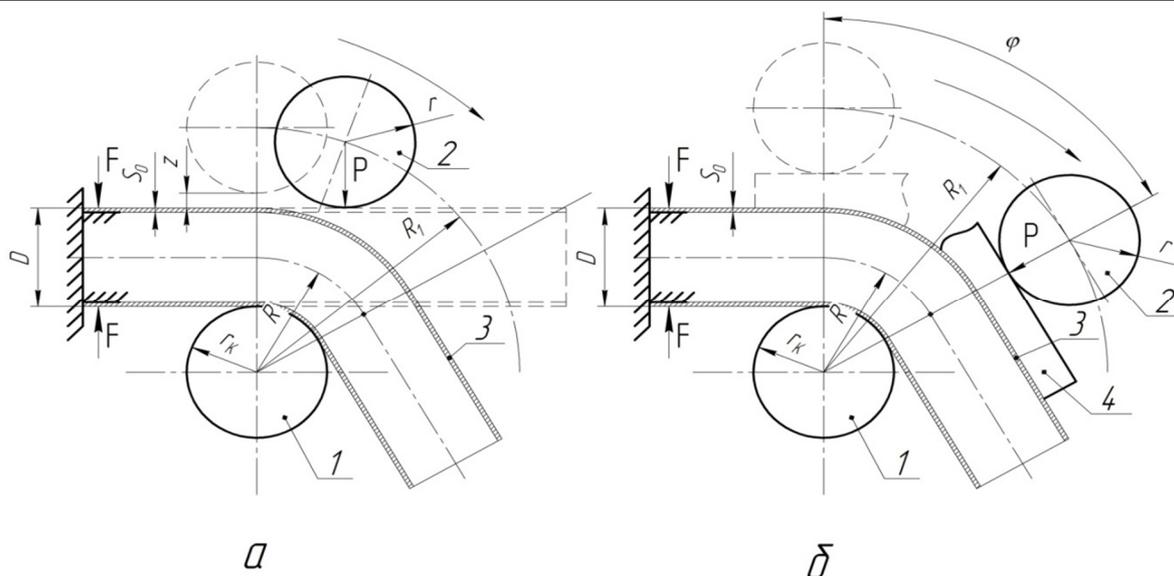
Схемы гибки обкаткой: а – с зазором z ; б – с использованием лотка
